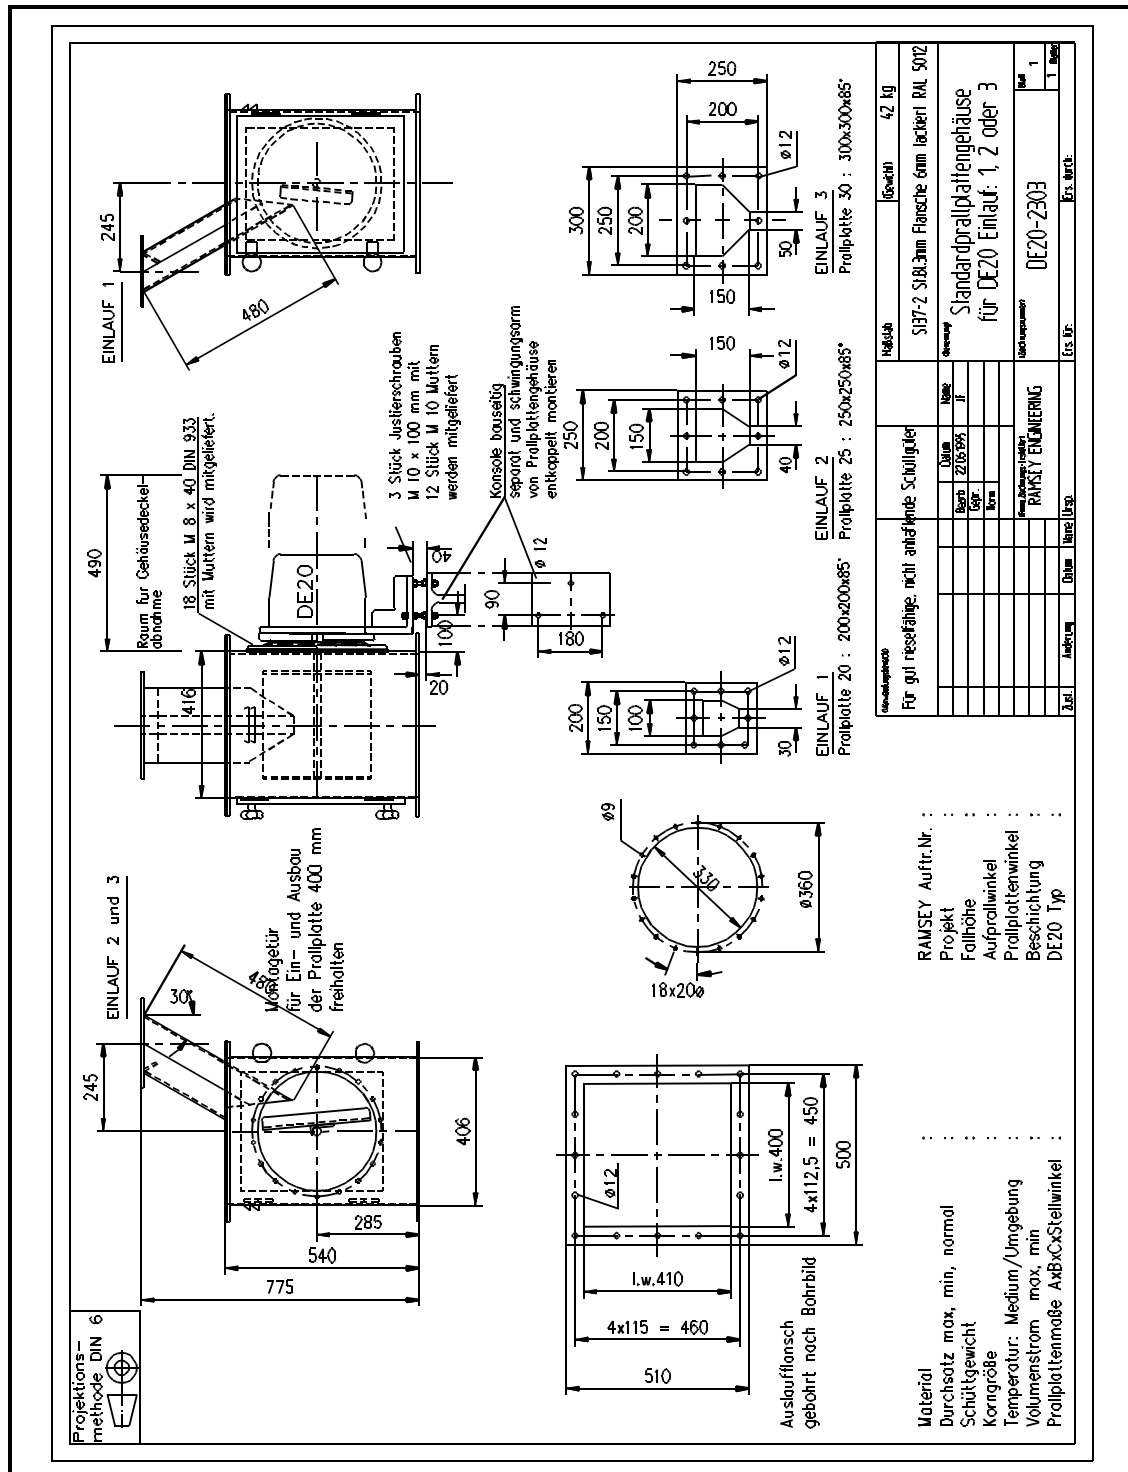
Einbauzeichnung Prallplattengehäuse und -sensor DE 20
